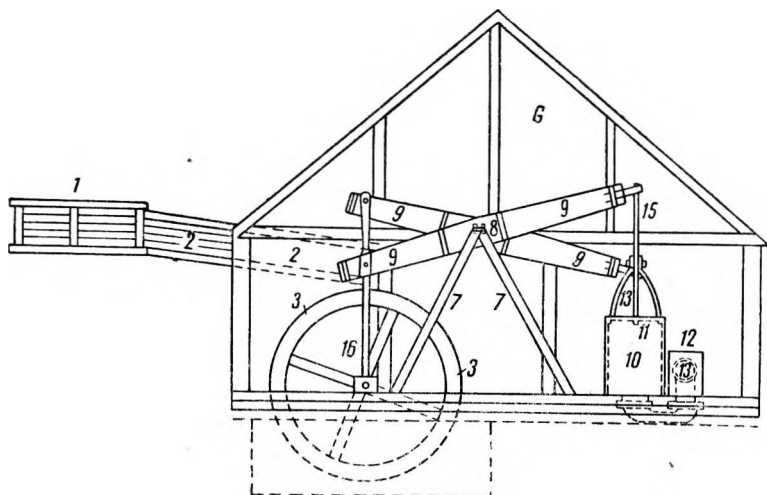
Водяной двигатель и цилиндрическая воздушная установка на Гавриловском заводе в 90-е гг. XVIII в. 1 — главный ларь; 2 — спуск для подачи воды на колесо; 3 — водяное колесо; 16 — шатуны; 9 — балансиры; 8 — подшипники балансиров; 15 — штанги для привода воздушного поршня; 10 — воздушный цилиндр; 11 — поршень; 12 — воздушный ларь; 13 — воздухопровод. (ЦГАНХ, Л.).
